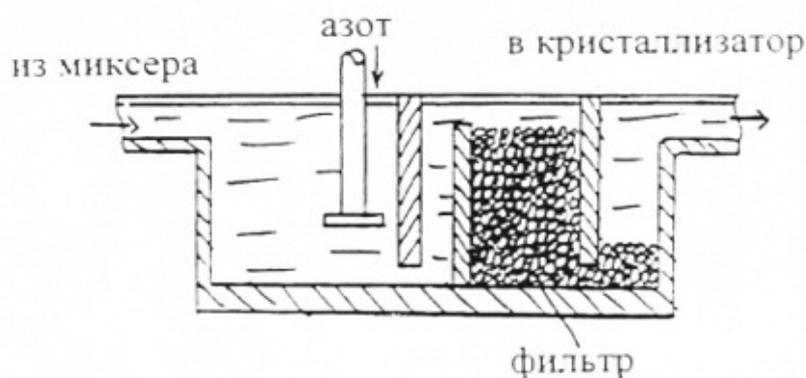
Схема установки для дегазации алюминиевых расплавов нейтральными газами с фильтрованием через оксид алюминия.
